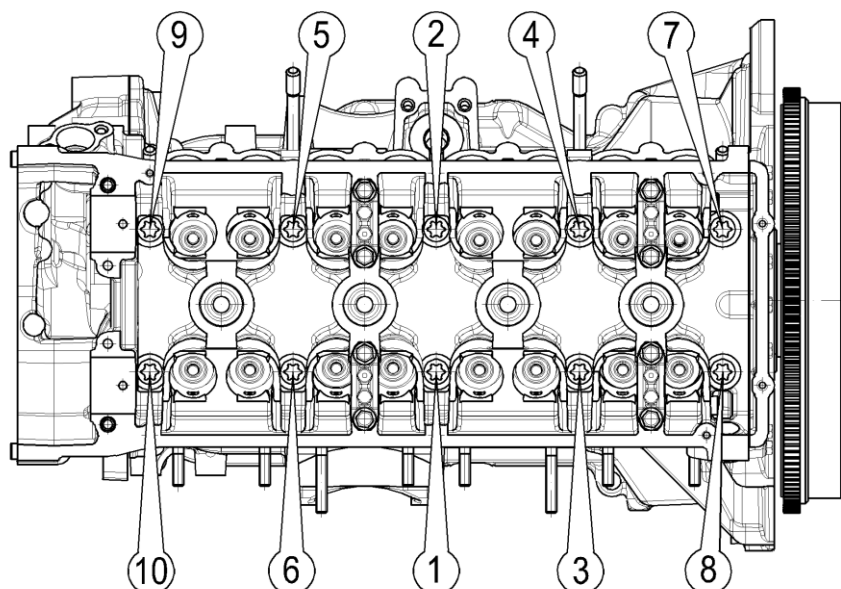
Последовательность затяжки болтов крепления головки цилиндров
